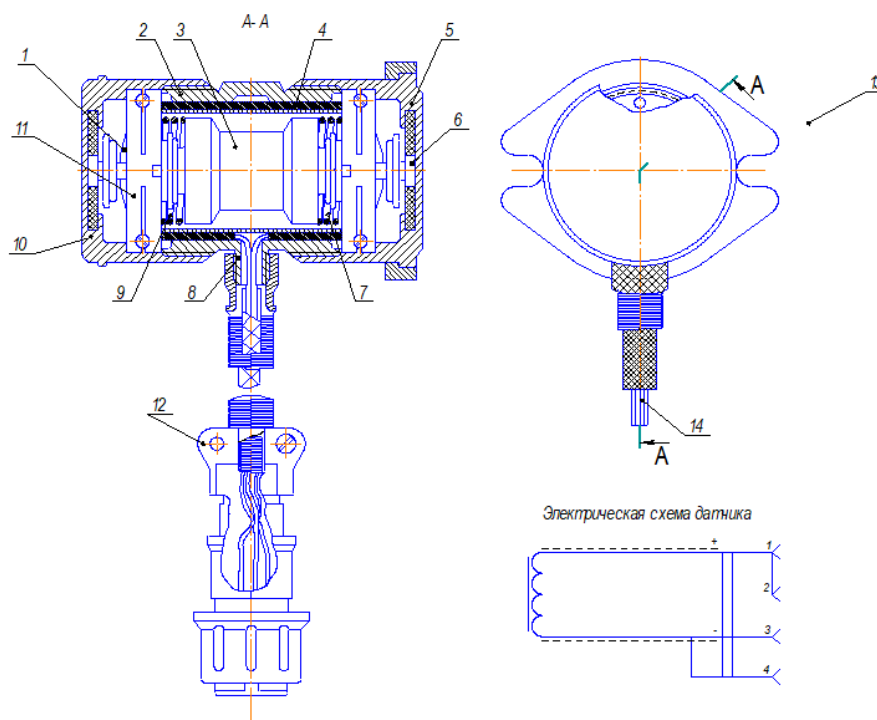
Датчик виброскорости: 1 – сектор; 2 – корпус; 3 – магнит; 4 – катушка; 5 – сектор; 6 – винт; 7, 9 – пружины; 8 – штуцер; 10 – крышка; 11 – подшипник; 12 – штеккер; 13 – фланец; 14 – соединительный кабель
